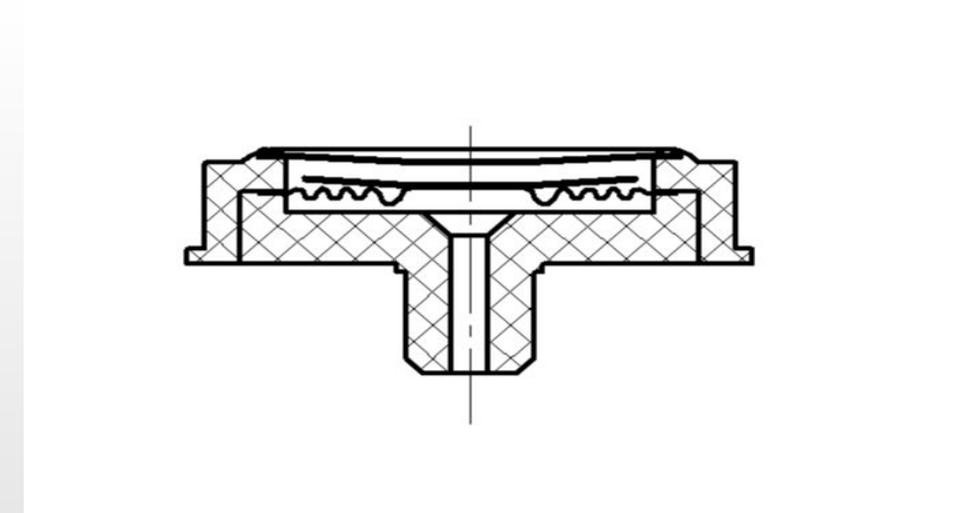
Общий вид емкостного преобразователя давления разрез
